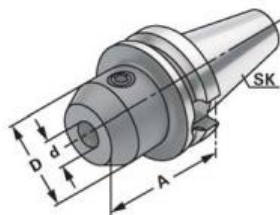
Оправка для кінцевої фрези DIN 1835 Form B [14]
